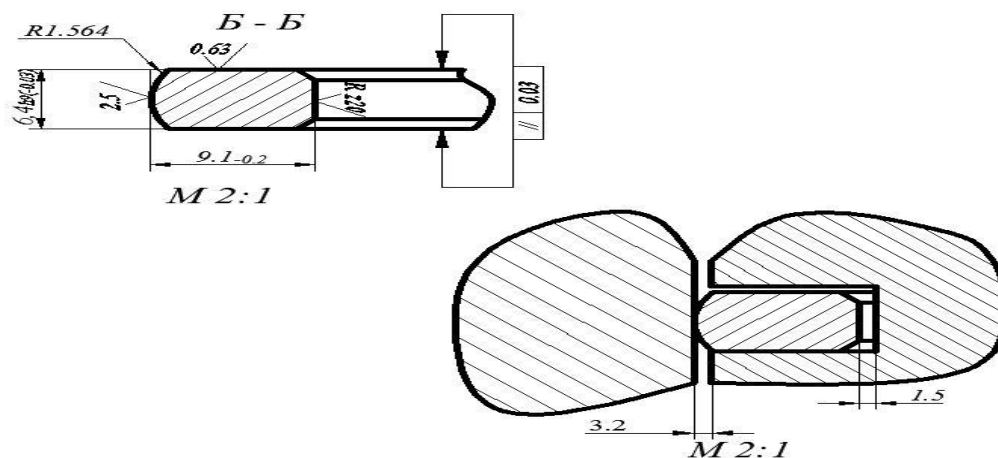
Компресійне кільце з бочкоподібною робочою поверхнею газового двигуна 6ГЧН 25/34
